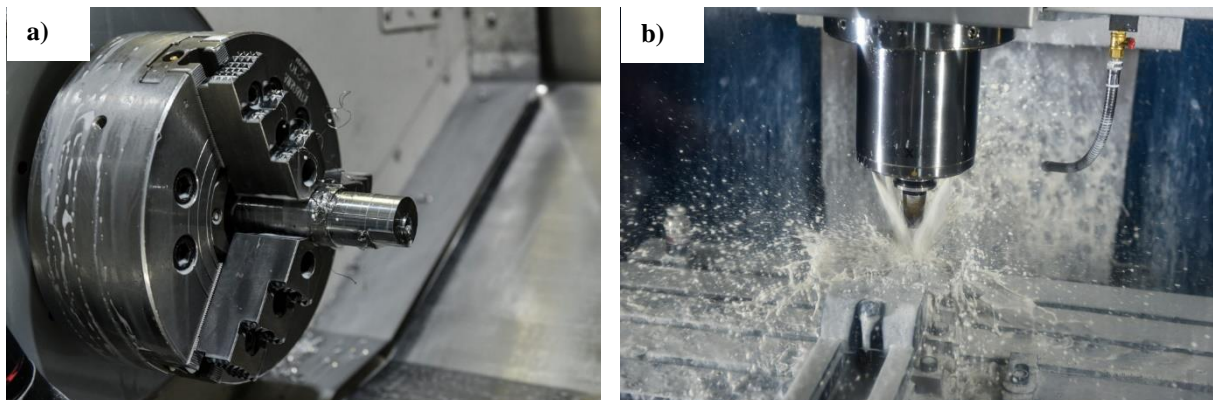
a) Peça em início da operação de torneamento.; b) Operação de fresagem.
